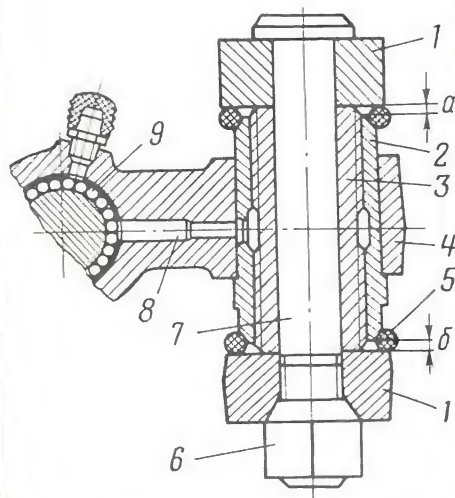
Разрез узла резьбового шарнира: 1 — головки рычагов передней подвески; 2 — наружная резьбовая втулка; 3 — распорная резьбовая втулка; 4 — головка стойки; 5 — защитное резиновое кольцо; 6 — специальная гайка; 7 — резьбовой палец; 8 — масляный канал; 9 — игольчатый подшипник; а и б — контрольные размеры.
